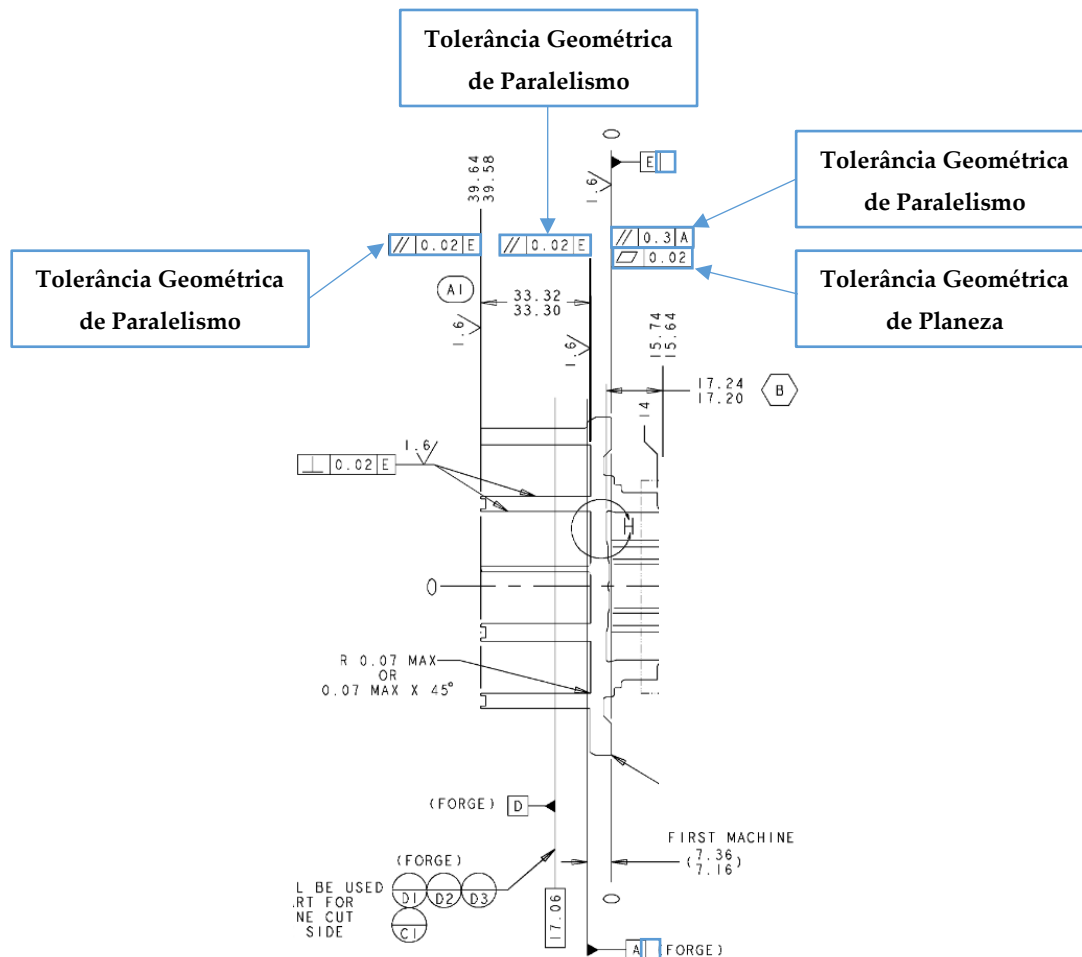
Desenho técnico com tolerâncias geométricas relativas ao componente em estudo.
